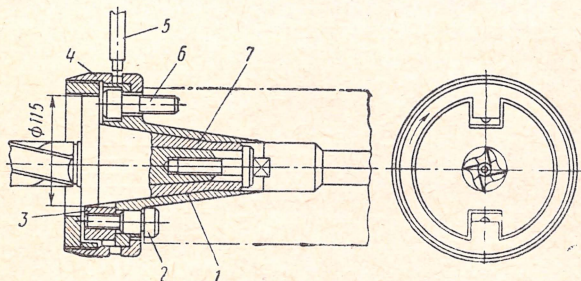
Патрон для безопасного крепления фрез на шпинделе фрезерного станка
